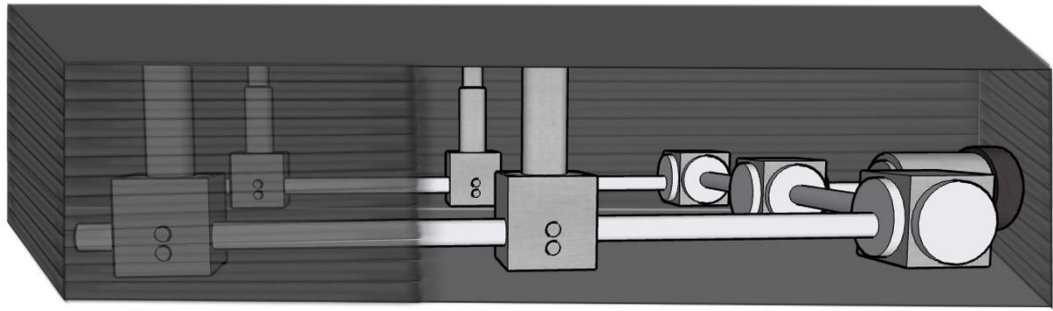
Sistema de U de elevadores cubierto con fuelle de PVC
